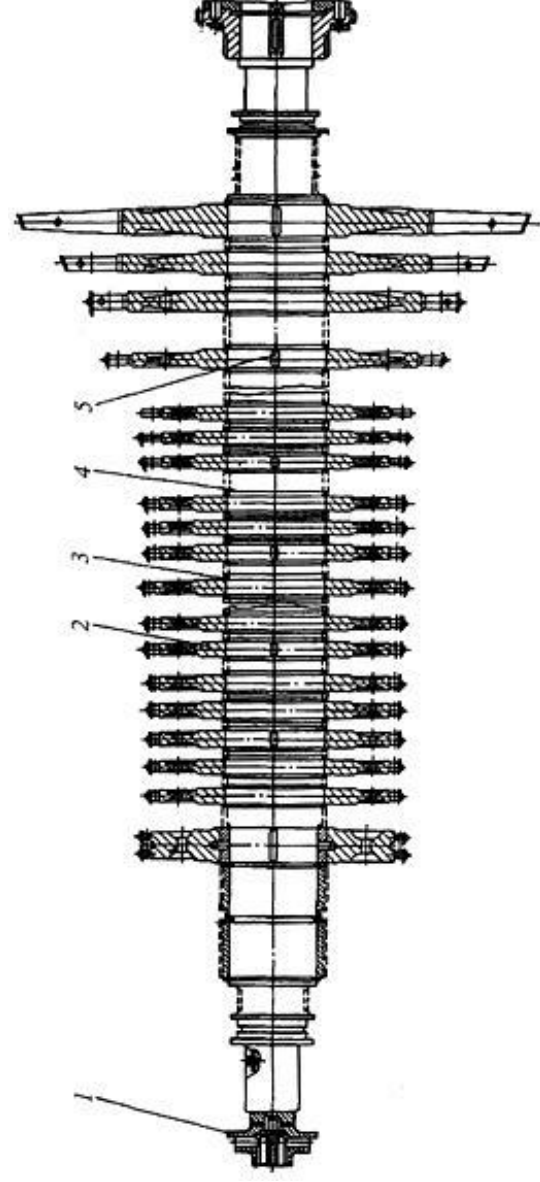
Составной ротор КТЗ: 1 – рабочее колесо главного масляного насоса; 2 – диск; 3 – кольцо; 4 – вал; 5 – осевая шпонка
